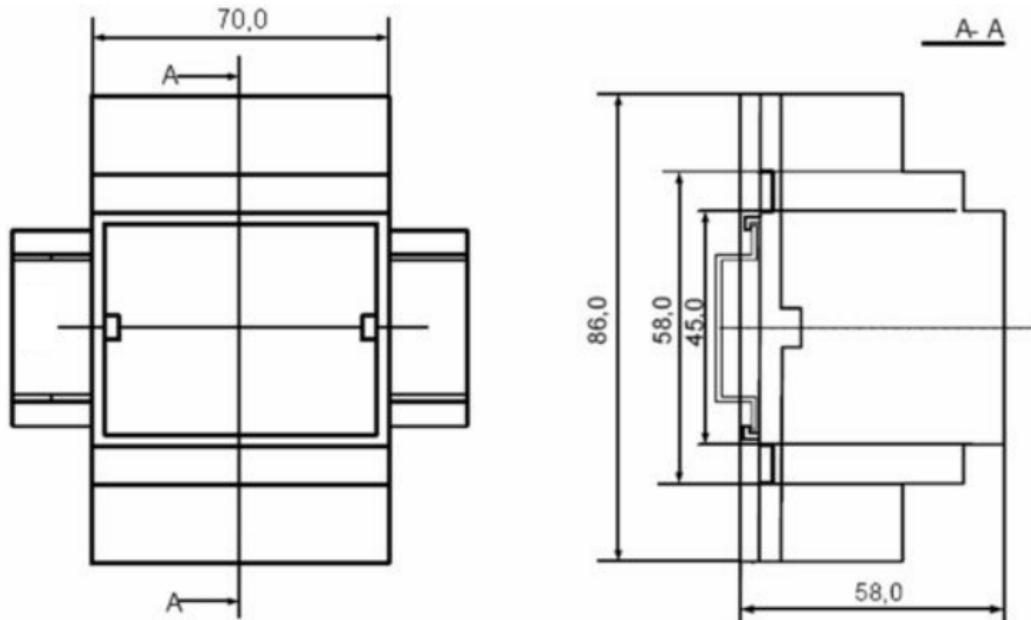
Габаритные и присоединительные размеры блока питания PSM-36-24
